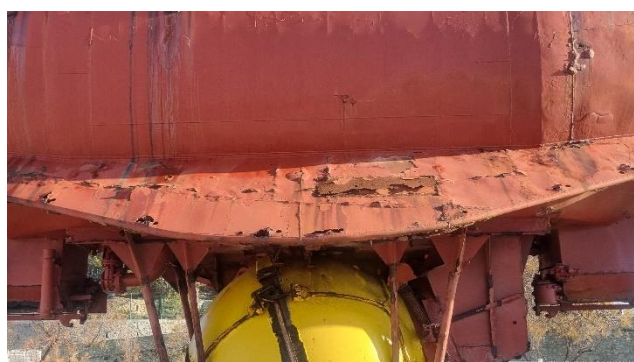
Vue générale du stabilisateur tribord, avec forte corrosion des tôles et des soudures entre tôles et corrosion perforante
